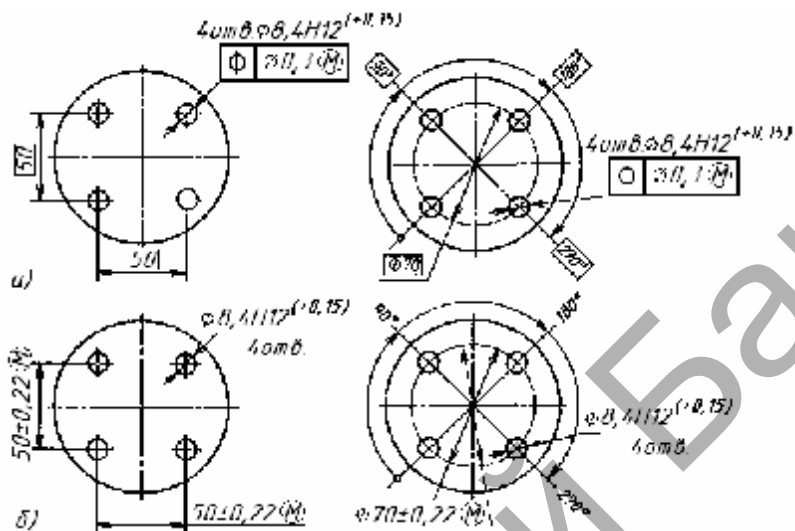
Пример назначения допусков расположения отверстий для крепления деталей типа крышек
